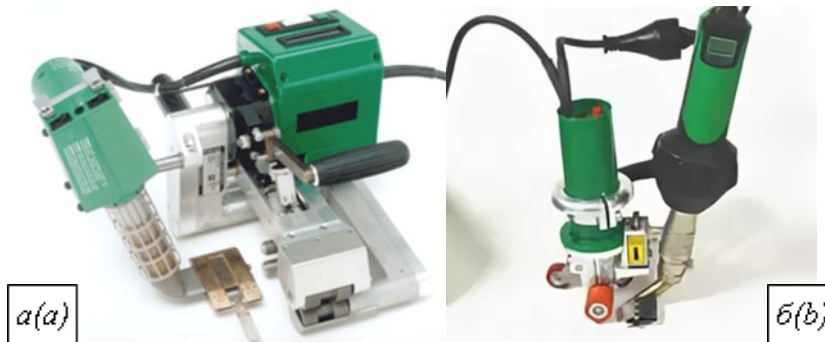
а – одна из моделей сварочного автомата горячего воздуха; б – пример полуавтоматического сварочного аппарата
